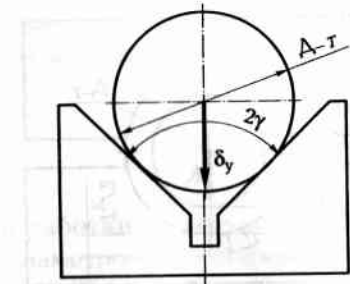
Схема установки цилиндрического вала на установочную призму
